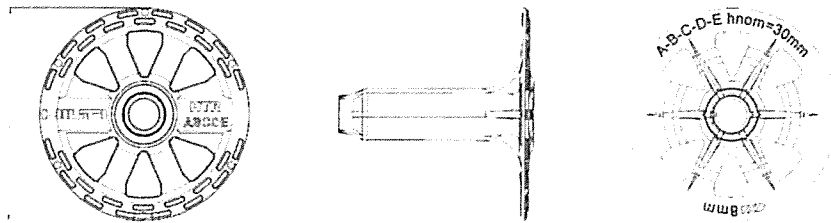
HTR-M - Zmontowana tuleja, talerzyk i wkręt kompozytowy
